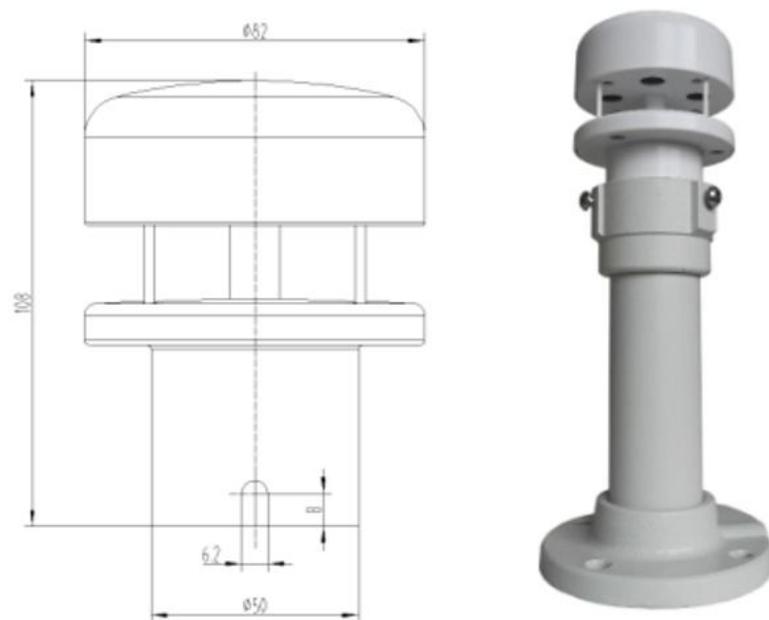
Габаритные размеры анемометра ІСВ-4Е
